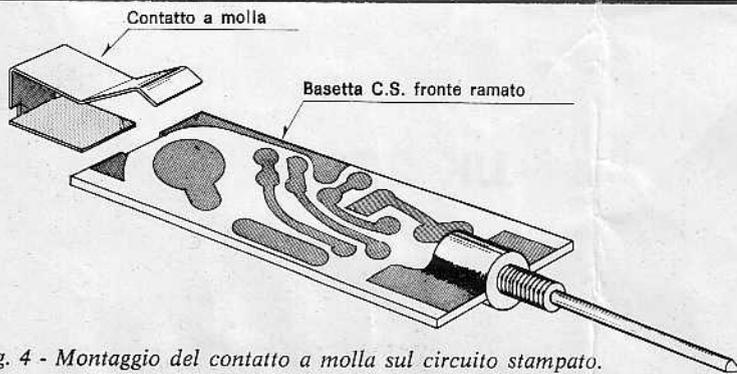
Montaggio del contatto a molla sul circuito stampato.
